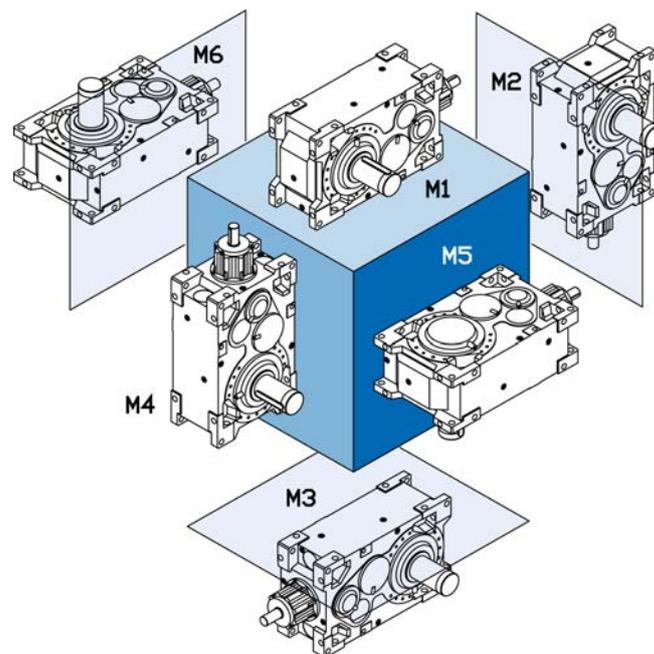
Positions de montage du réducteur à couple conique avec surface de montage standard
